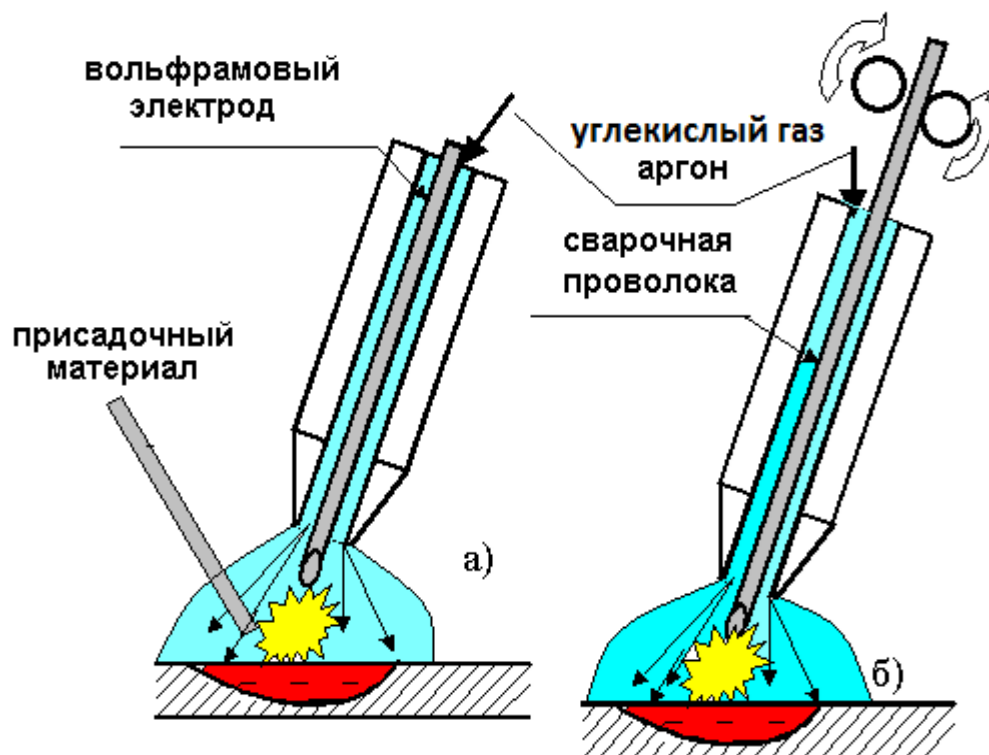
Схемы сварки в среде защитных газов
